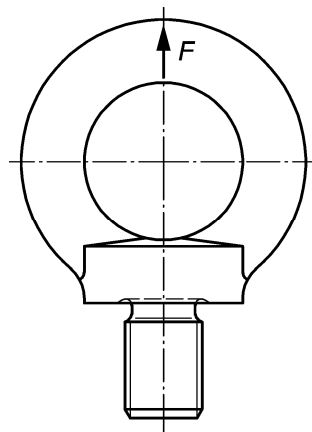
Beispiel für Kennzeichnung von Ringschrauben
